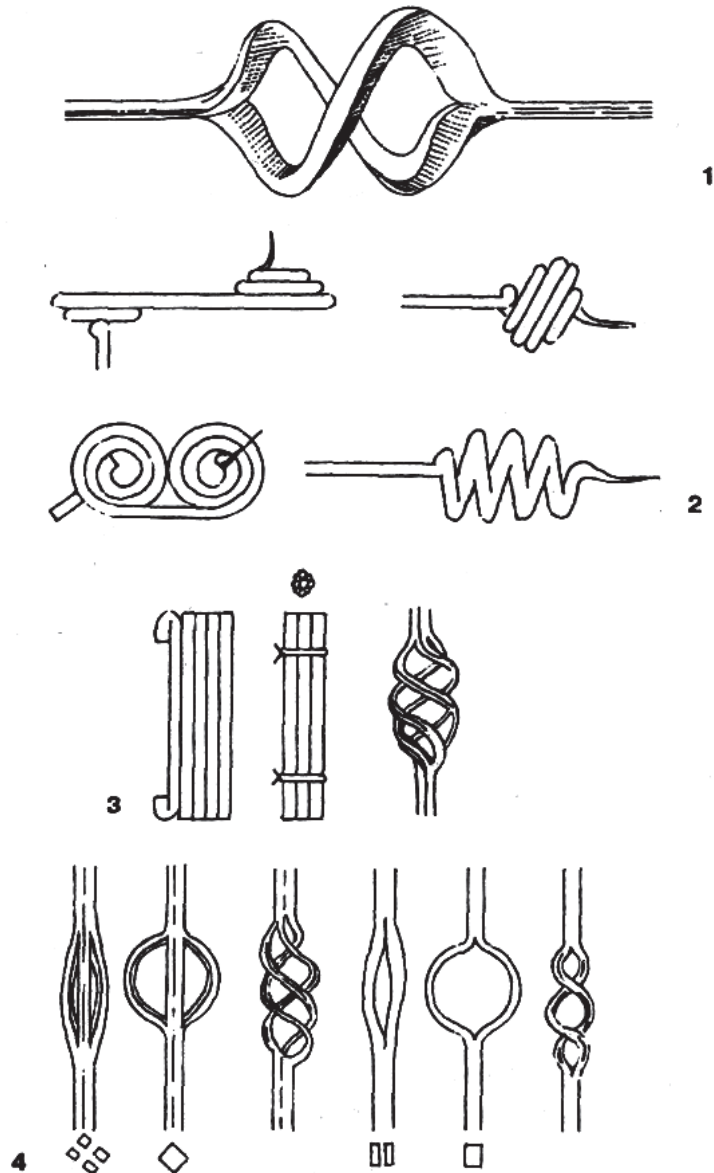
Шишка: 1 – із просіченої заготовки; 2 – скручена з одного прутка; 3 – зі зв'язаних прутків; 4 – із просіченої смугової заготовки
